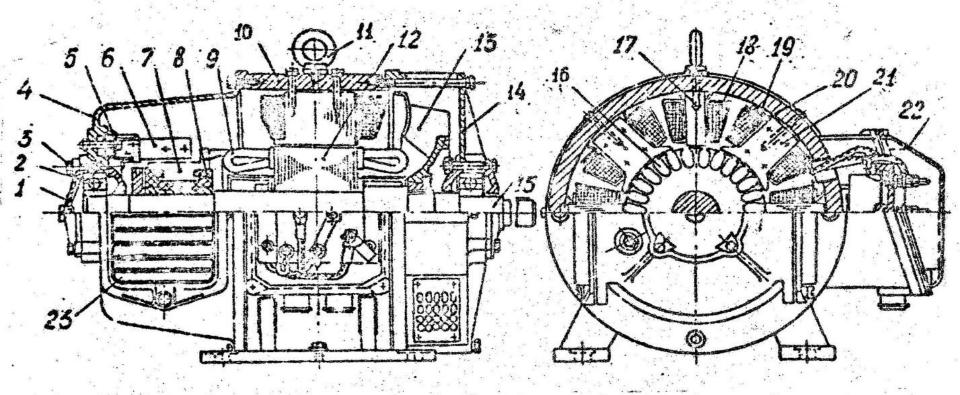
Продольный и поперечный разрезы машины постоянного тока серии П: I - крышка подшипника; 2 - шариковый подшипник; 3 - болт траверсы; 4 - передний подшипниковый щит; 5 - траверса; 6 - палец щеткодержателя; 7 - коллекторная пластина; 8 - пластмасса; 9 - лобовые части обмотки; 10 - ярмо; II - рым; I2 - сердечник ротора; I3 - вентилятор; I4 - задний подшипниковый щит; I5 - вал; I6 - паз ротора; I7 - сердечник дополнительного полюса; I8 - катушка сополнительного полюса; I9 - последовательная обмотка возбуждения; 20 - параллельная обмотка возбуждения; 21 - сердечник главного полюса; 22 - коробка выводов; 23 - щиток
